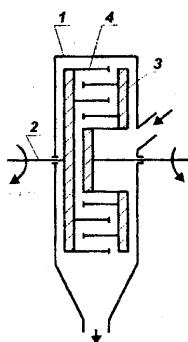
Дезінтэгратар: 1 — корпус; 2 — вал; 3 — дыск; 4 — пальцы
